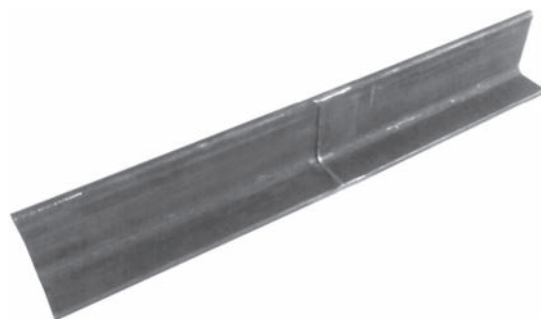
Сварное соединение таврового профиля из алюминиевого сплава В95Т1
